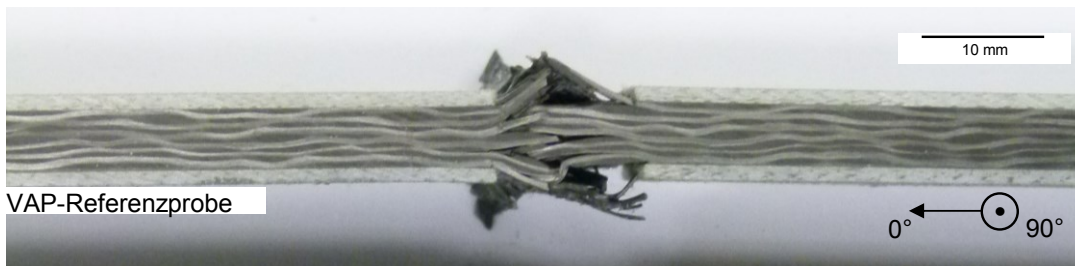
Bruchbild einer VAP-Referenzdruckprobe
